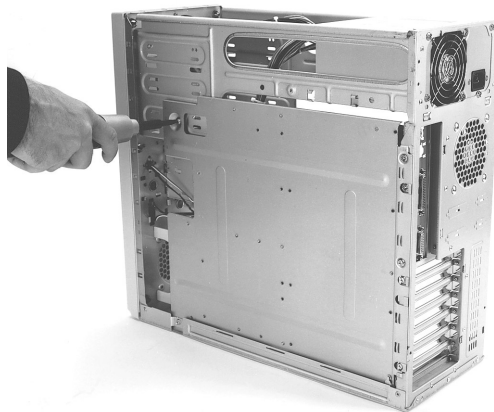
Осталось лишь привинтить шасси к корпусу
